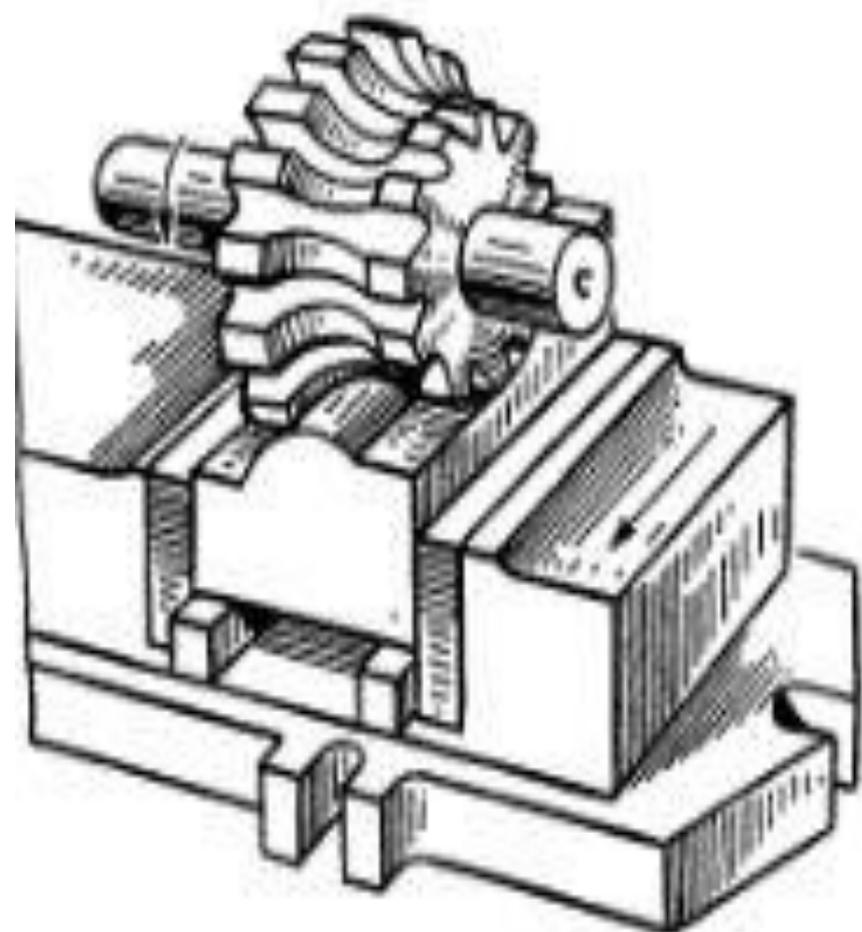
Фрезерование фасонной поверхности фасонной фрезой
